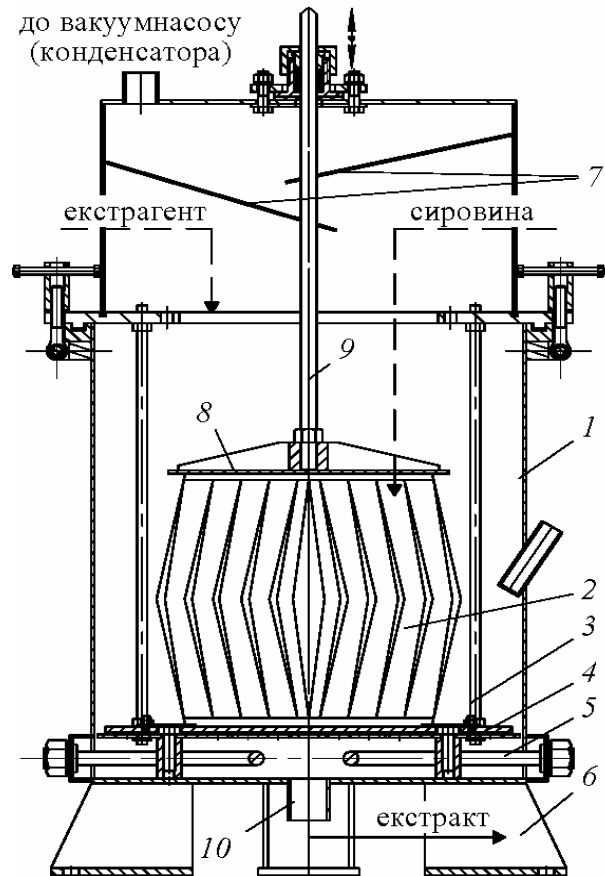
Принципова схема віброекстрактора з гнучким контейнером: 1 – корпус; 2 – віброперемішувальний пристрій (контейнер); 3 – напрямна штанга; 4 – перфорований диск – основа; 5 – нагрівальний елемент; 6 – опора; 7 – лабиринтний бризкоуловлювач; 8 – тарілка; 9 – шток; 10 – штуцер
